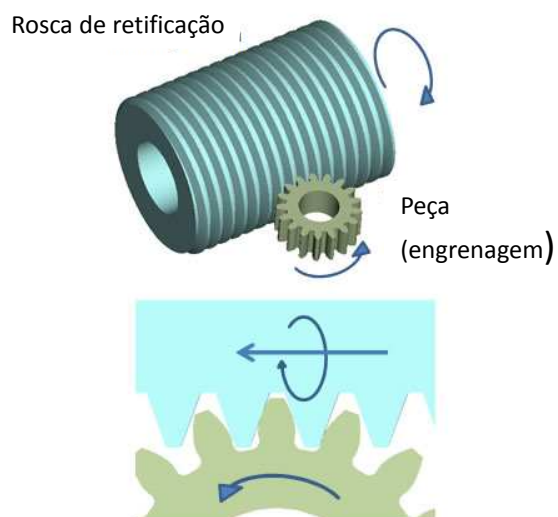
Formação de uma engrenagem por esmerilhamento. Fonte: <https://www.yanmar.com/eu/Technology/YANMAR-Technical-Review/Introduction-to-Machine-Tools-Used-in-Gear-Processing/>
